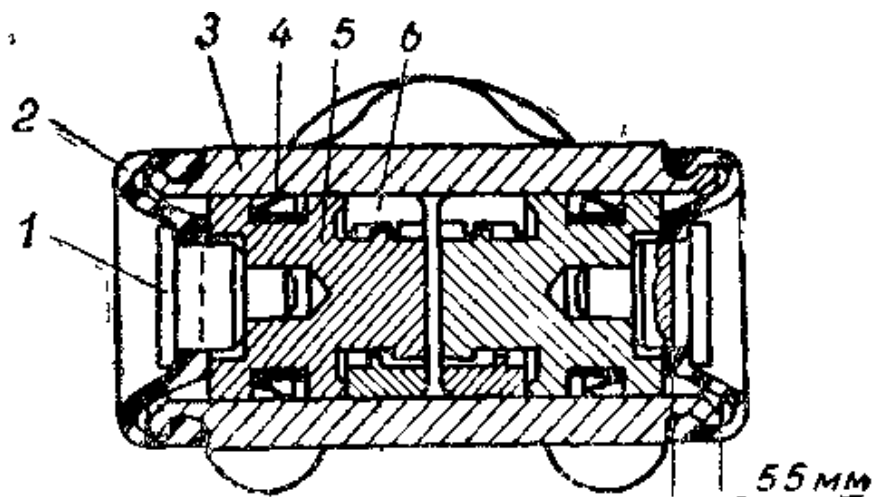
Колесный тормозной цилиндр с устройством для автоматической регулировки зазоров между колодками и барабаном
